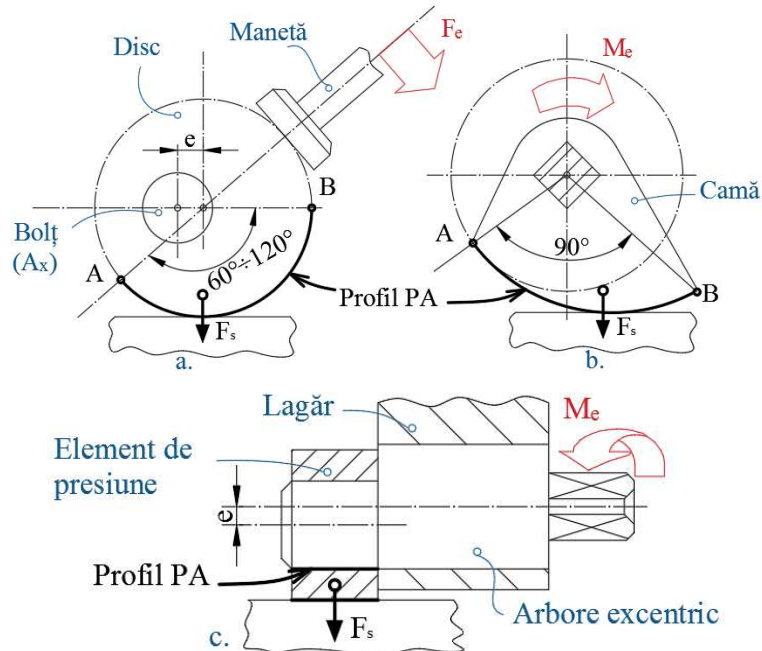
Variante constructive uzuale ale mecanismelor cu camă
